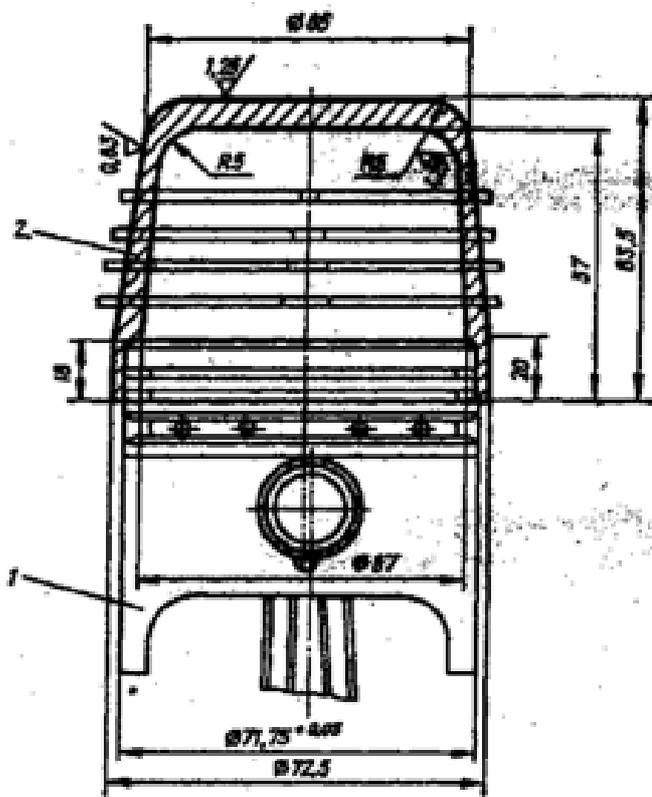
Оправка для надевания на поршень поршневых колец: 1 - поршень; 2 - оправка М9840-731
